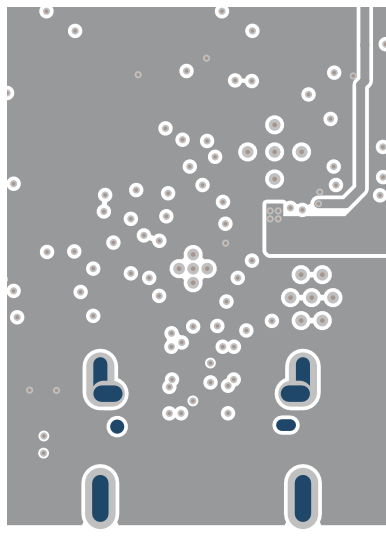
TPS26750 PCB Layout - Signal Layer 4
